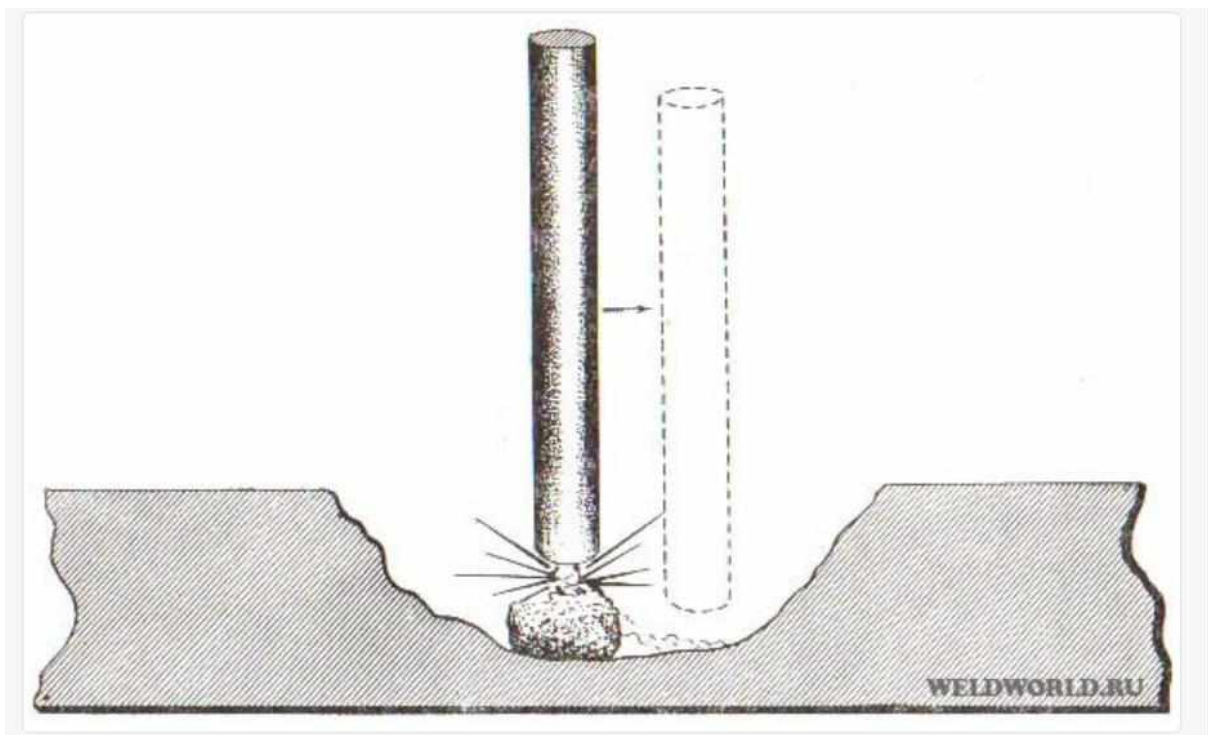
Soldagem com eletrodo metálico com abertura de arco em um suporte de carbono – Weldworld.ru
